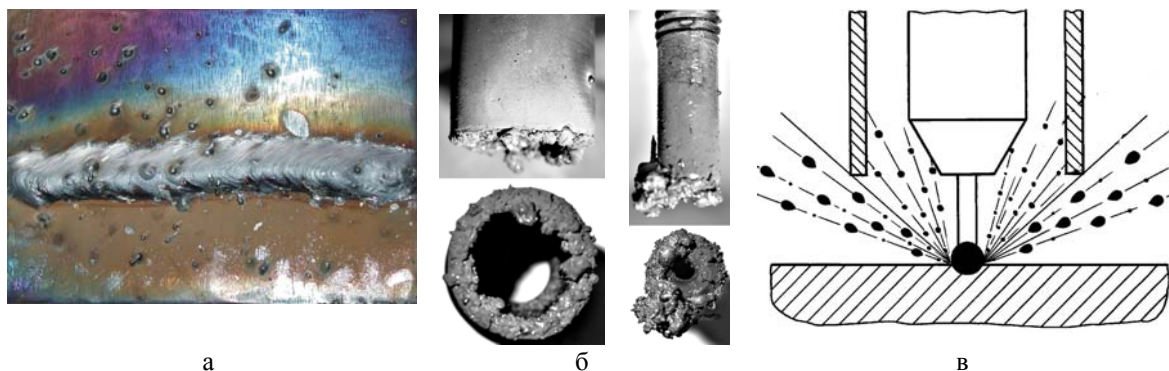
а) набрызгивание на сварное соединение; б) забрызгивание деталей сварочной горелки; в) схема разбрызгивания электродного металла при сварке.
